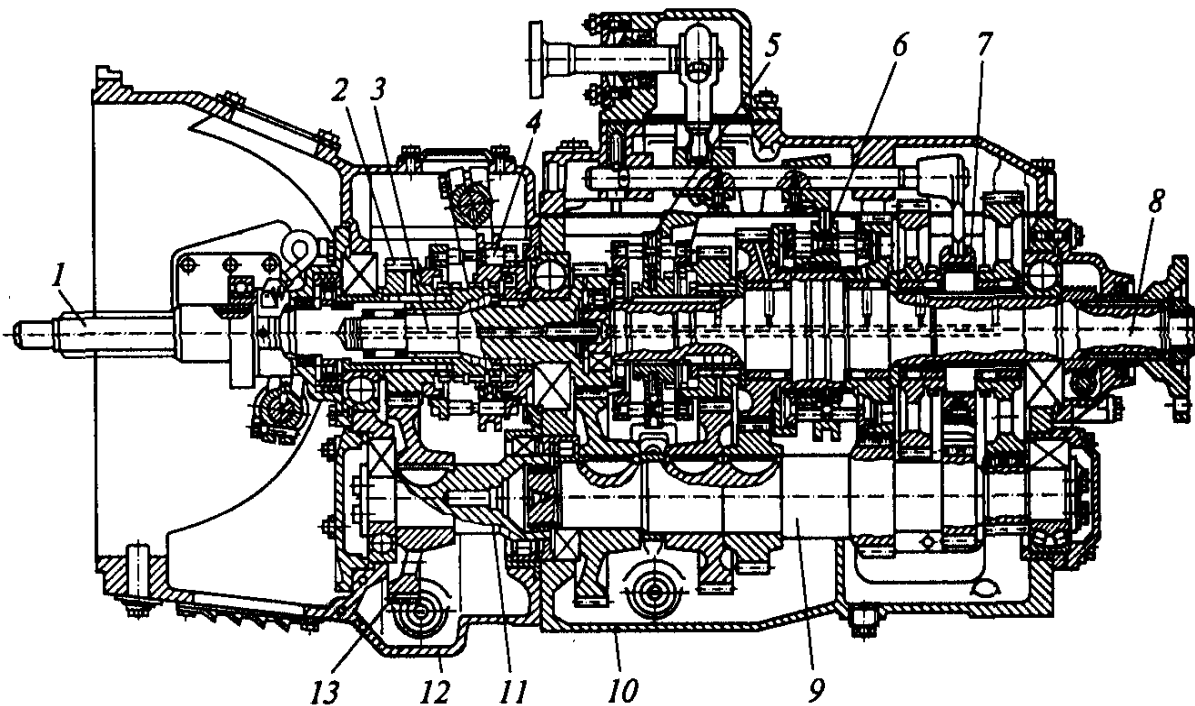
Коробка передач грузовых автомобилей КамАЗ:
